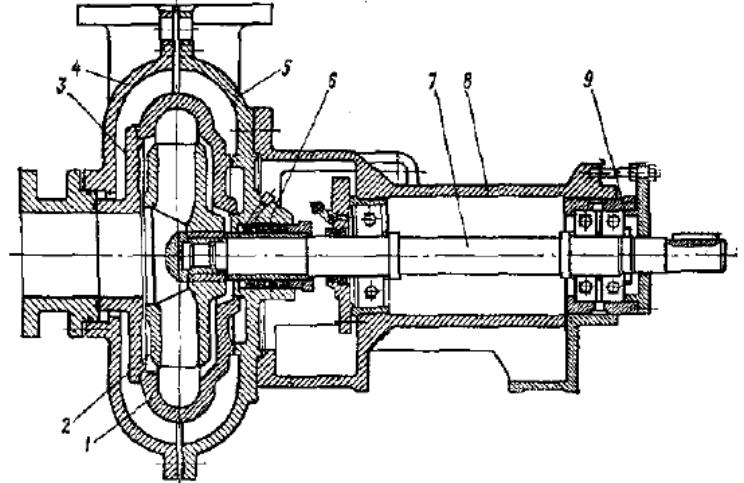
Двокорпусний ґрунтовий насос: 1 – внутрішній корпус; 2 – робоче колесо; 3 – захисний диск; 4 – передня половина корпусу; 5 – задня половина корпусу; 6 – сальник; 7 – вал; 8 – опорний кронштейн; 9 – стакан для регулювання осевого переміщення
